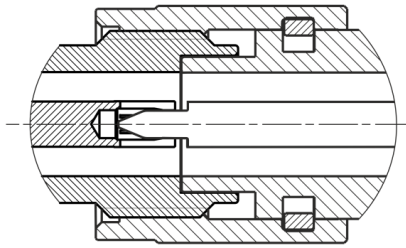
Соединители тип 3,5 мм и IX (розетка слева, вилка справа)
